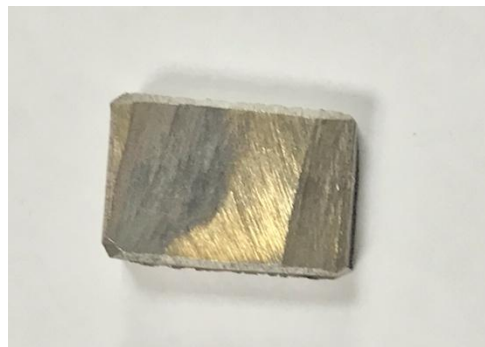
Образец нержавеющей стали марки 12X18H12T
